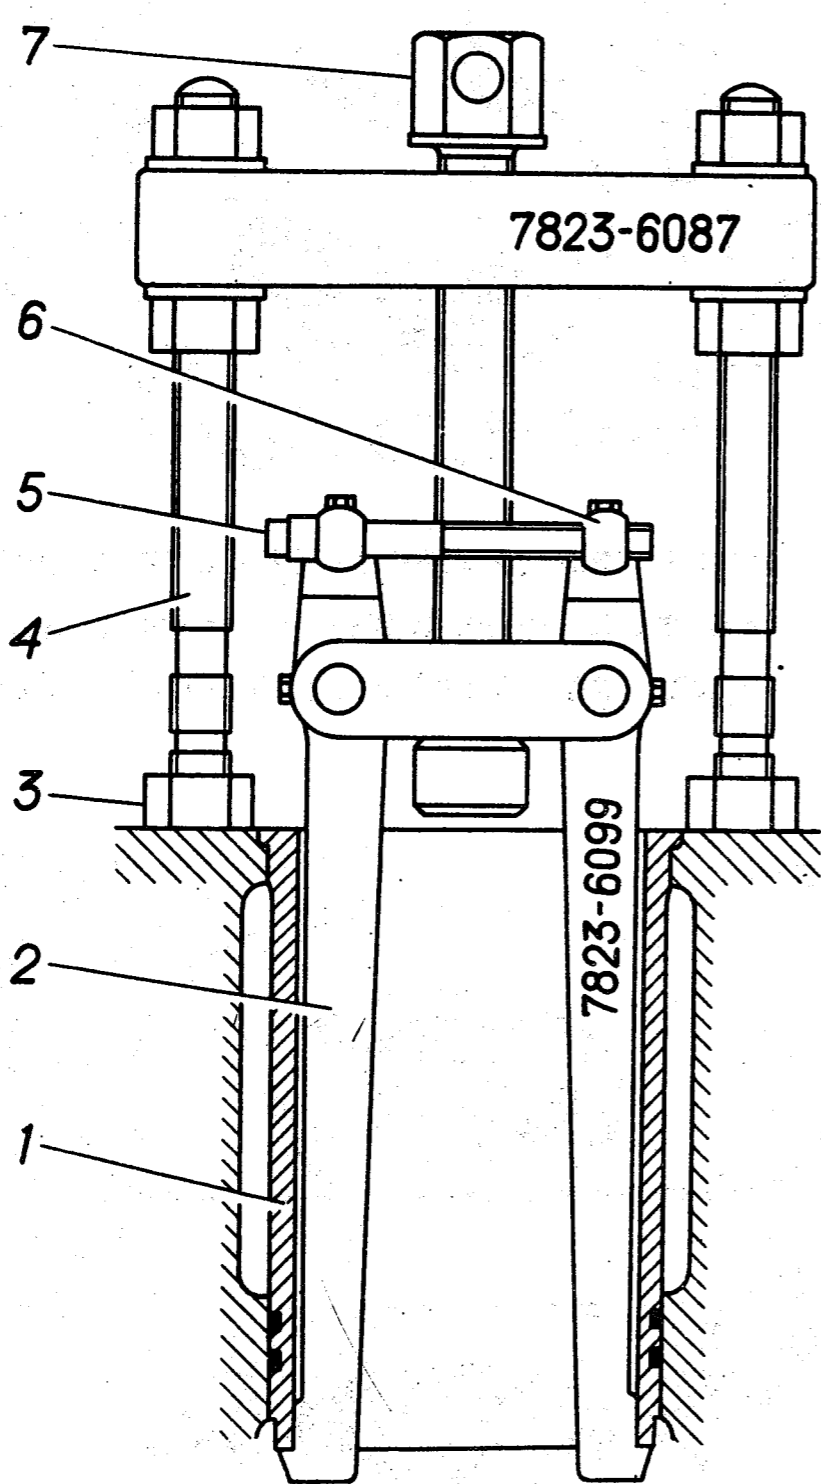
Выпрессовка гильзы из блока цилиндров комбинированным съемником:
